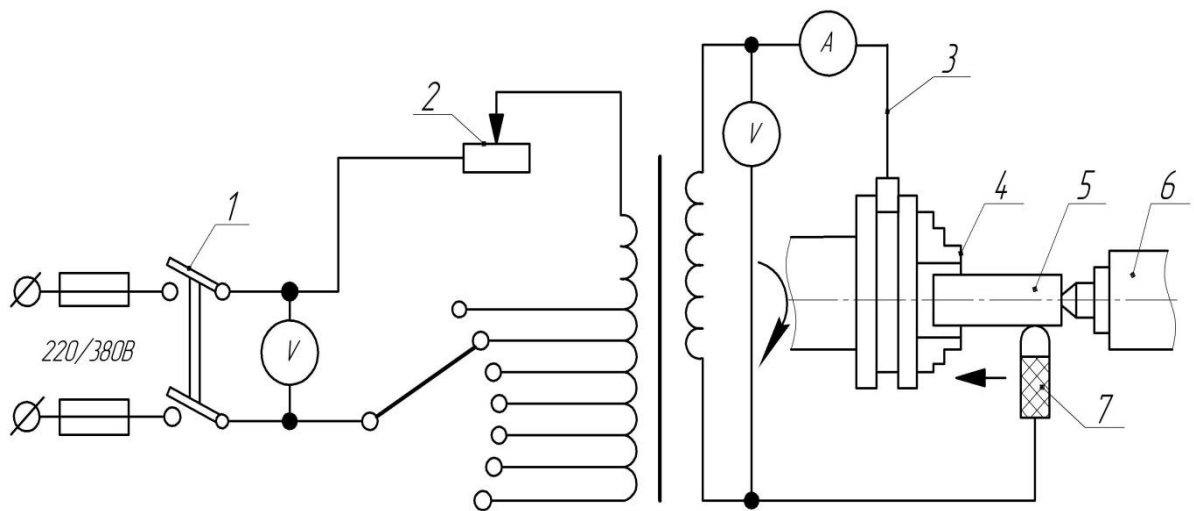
Принципова схема установки для електромеханічної обробки:
